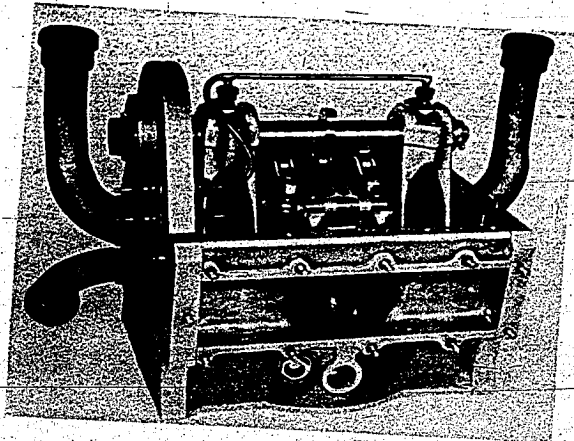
Zylinderkopf des I.C.-Versuchsmotors mit Jumo-211 A-Zylinder
